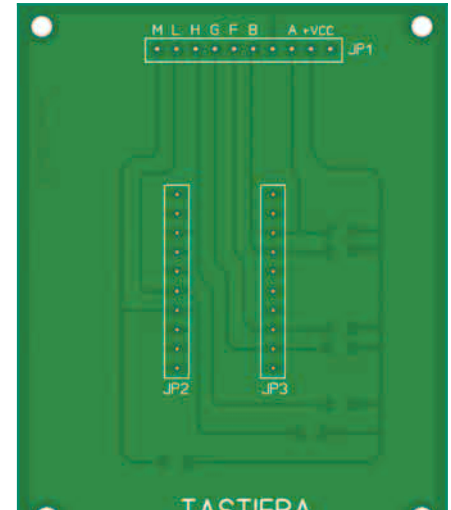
Piano di montaggio lato componenti del modulo tastierino
